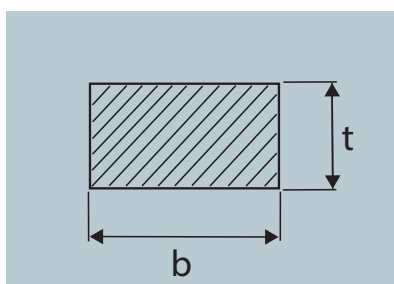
Warmgewalzter Flachstahl: Profilabmessungen
